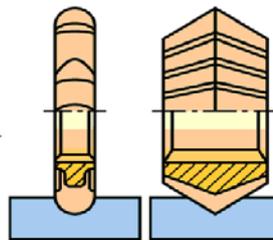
Плоское фрезерование торцевой фрезой
